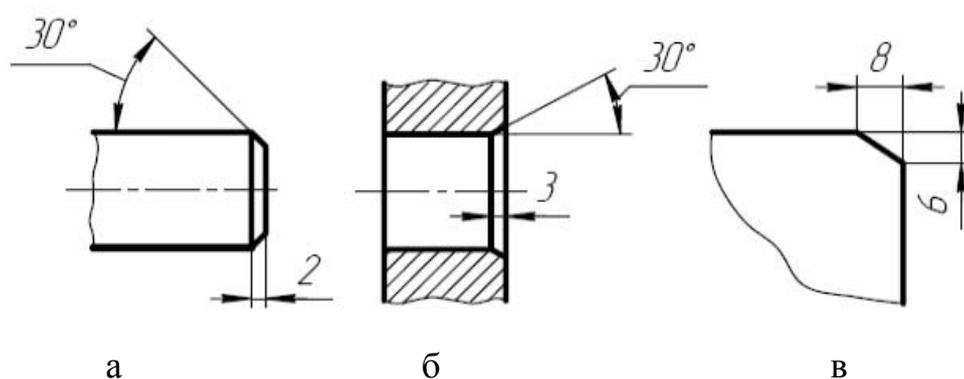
Нанесение размеров фасок под углом, отличным от 45°
